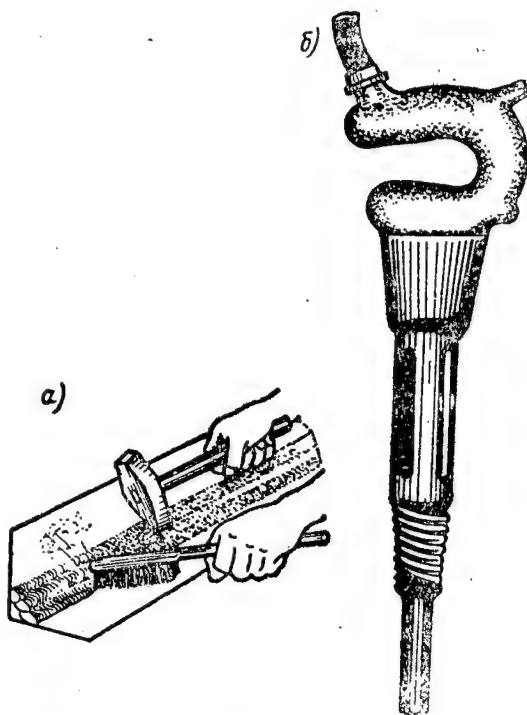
Инструмент для чистки металла и обивки шлака сварных швов
